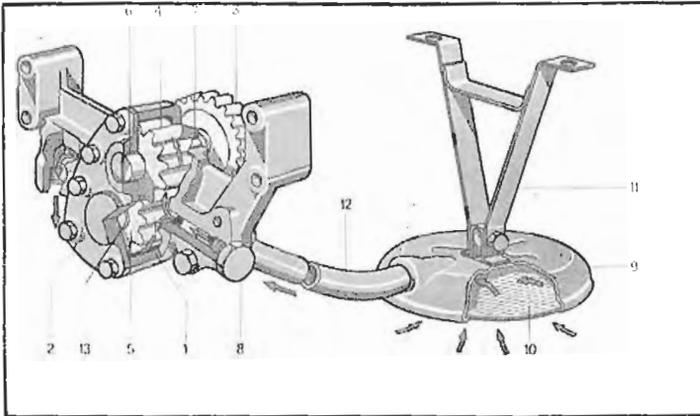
Conjunto de bomba y colador (UTB). 1.- Cuerpo bomba. 2.- Tapa. 3.- Engranaje de mando. 4.- Piñón conductor. 5.- Piñón conducido. 6-7.- Espacio interior de la bomba. 8.- Tapón. 9.- Colador. 10.- Taziz. 11.- Soporte. 12.- Tubería de aspiración.
